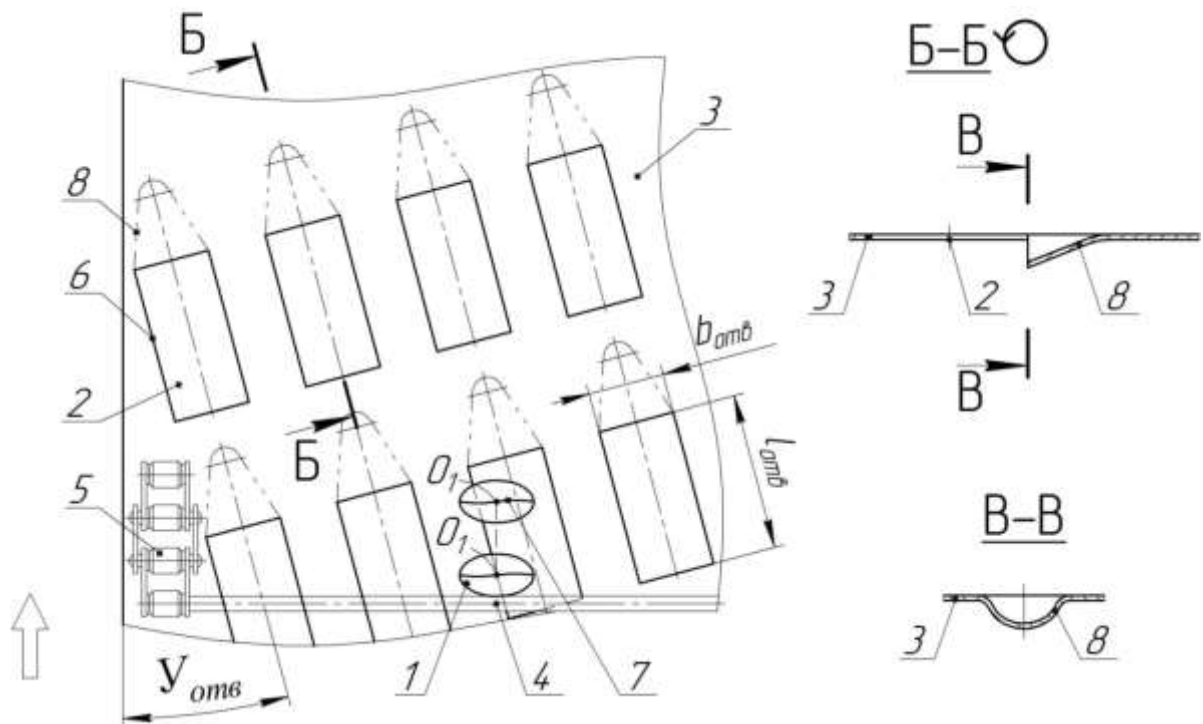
Расположение отверстий решетчатого днища под острым углом к направлению движения скребков транспортера: 1 – зерно; 2 – отверстие; 3 – днище; 4 – скребок; 5 – плавающий транспортер; 6 – боковая кромка отверстия; 7 – положение зерна при его опрокидывании; 8 – выемка
